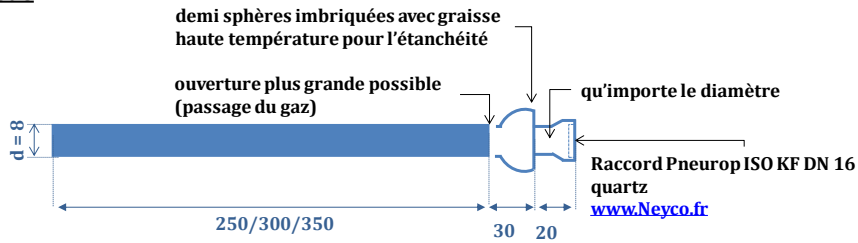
Dimensions des pièces du réacteur a lit fixe
